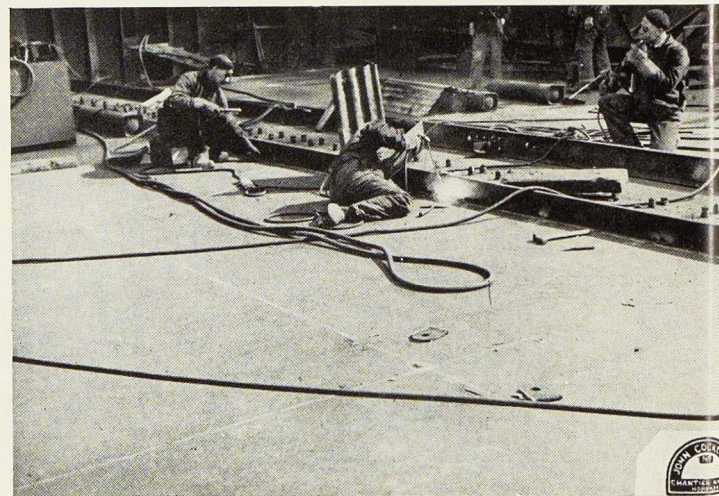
Soudage d'un joint de pont de cargo soudé (chantier John Cockerill).
